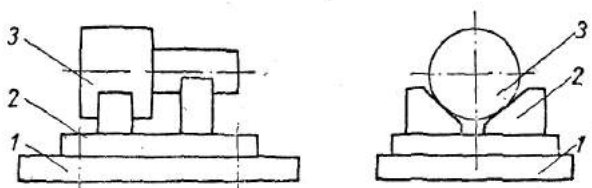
Приклад розміщення заготовки на тактовому столі:
